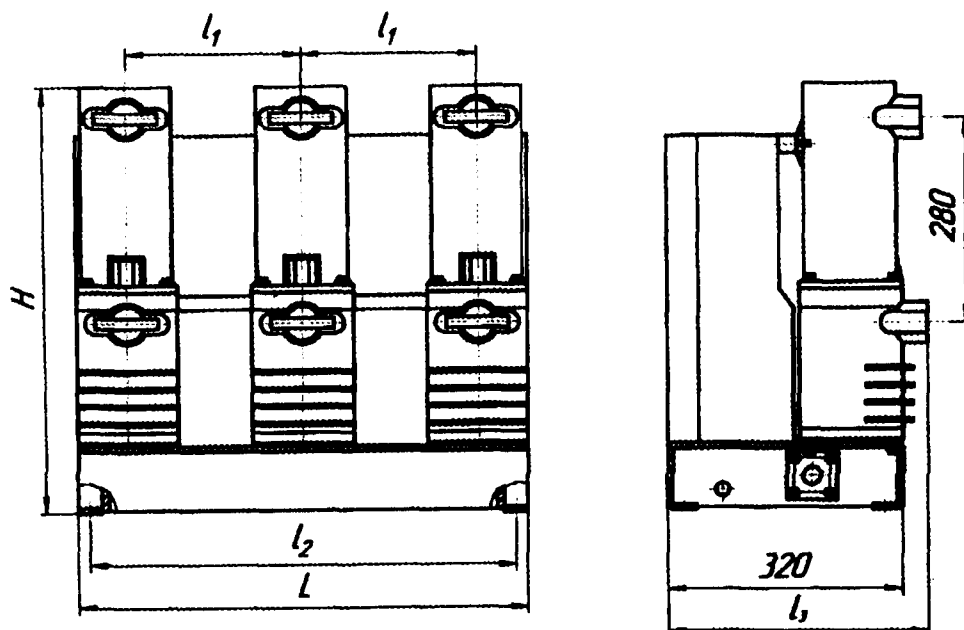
Общий вид и габаритные размеры ВБ-10-20/630-1600 УХЛ2
